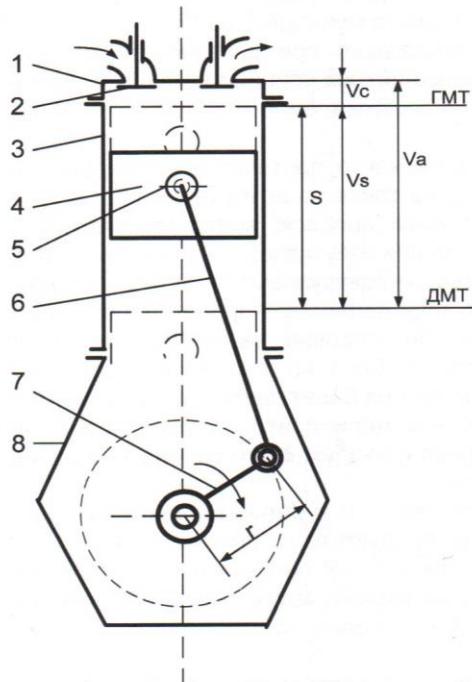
Бутален двигател: 1-цилиндрова глава; 2-клапани; 3-цилиндър; 4-бутало; 5-бутален болт; 6-мотовилка; 7-колянов вал; 8-картер; 9-маховик.
